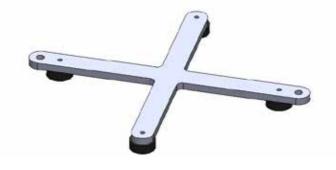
Установка основания Вид снизу (рисунок 125):
